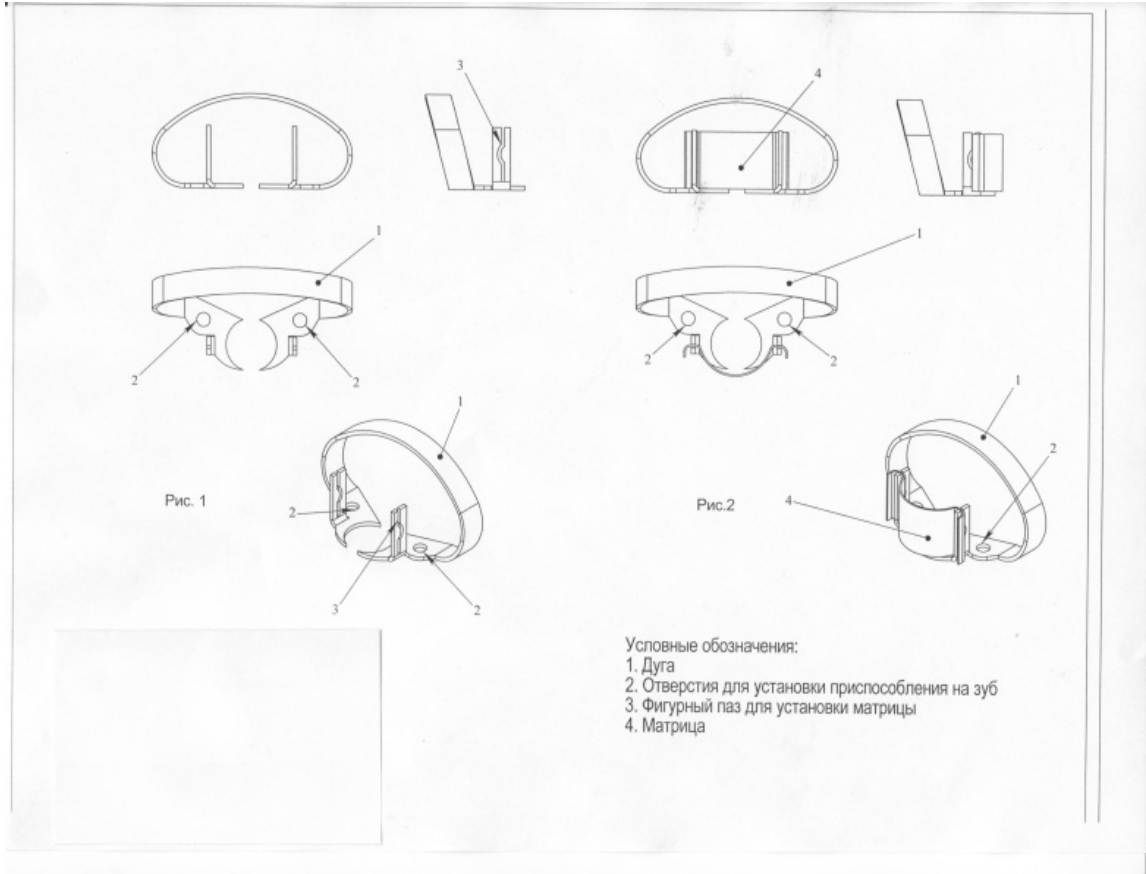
Чертёж приспособления для защиты проксимальных поверхностей зубов
